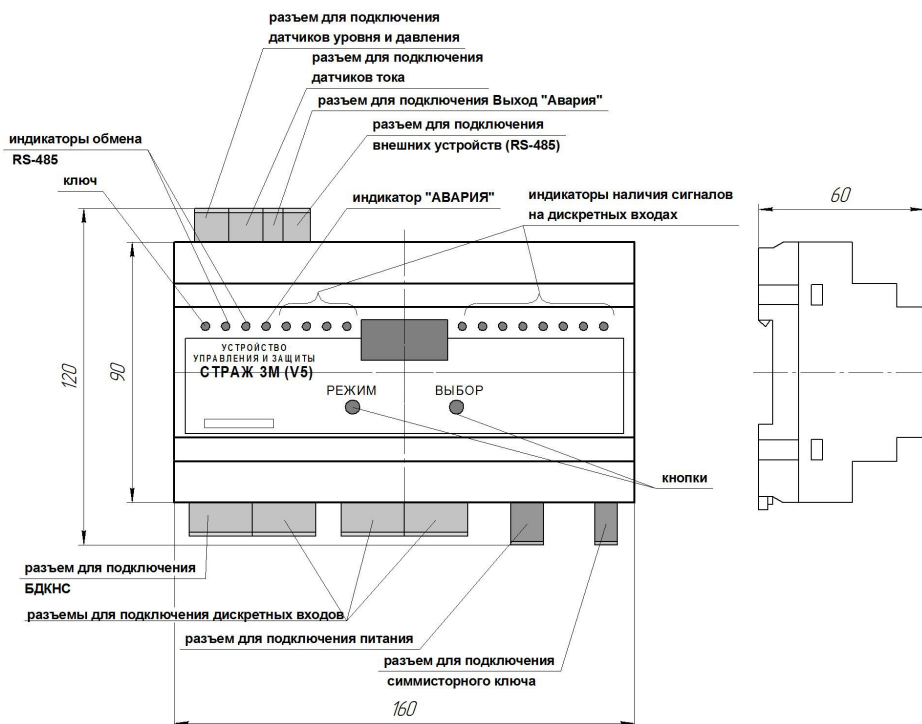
Внешний вид устройства управления и защиты СТРАЖ 3М(V5)
